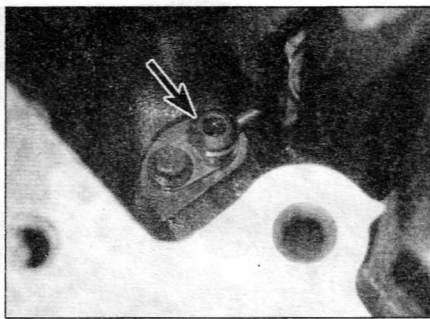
Трубка масляной форсунки для смазывания поршня (отмечена стрелкой) в блоке цилиндров
